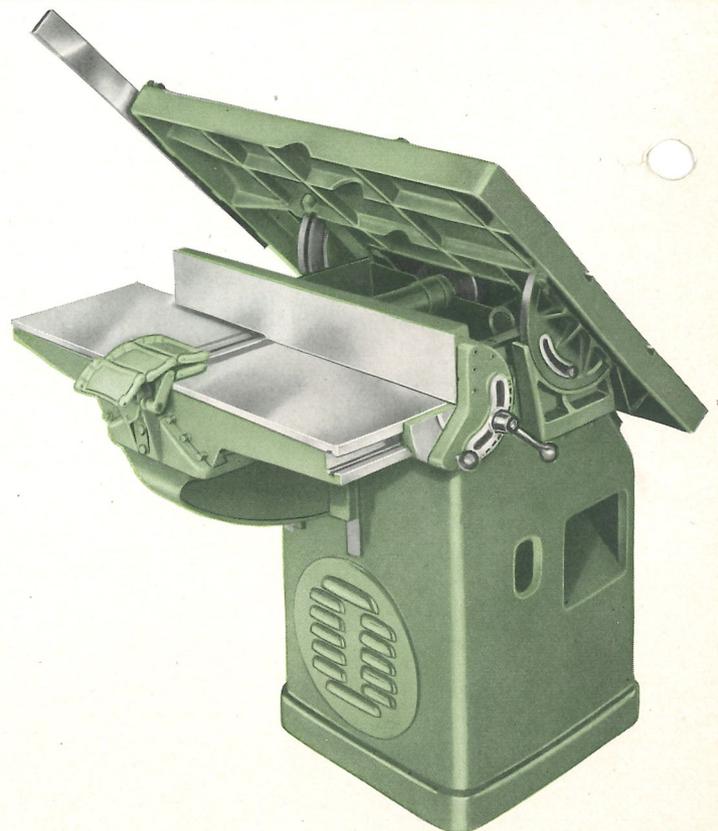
Type 630 mit Schwenkeinrichtung und Hobelapparat
